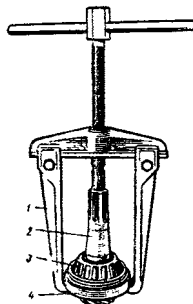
Снятие внутреннего кольца заднего подшипника ведущей шестерни главной передачи
